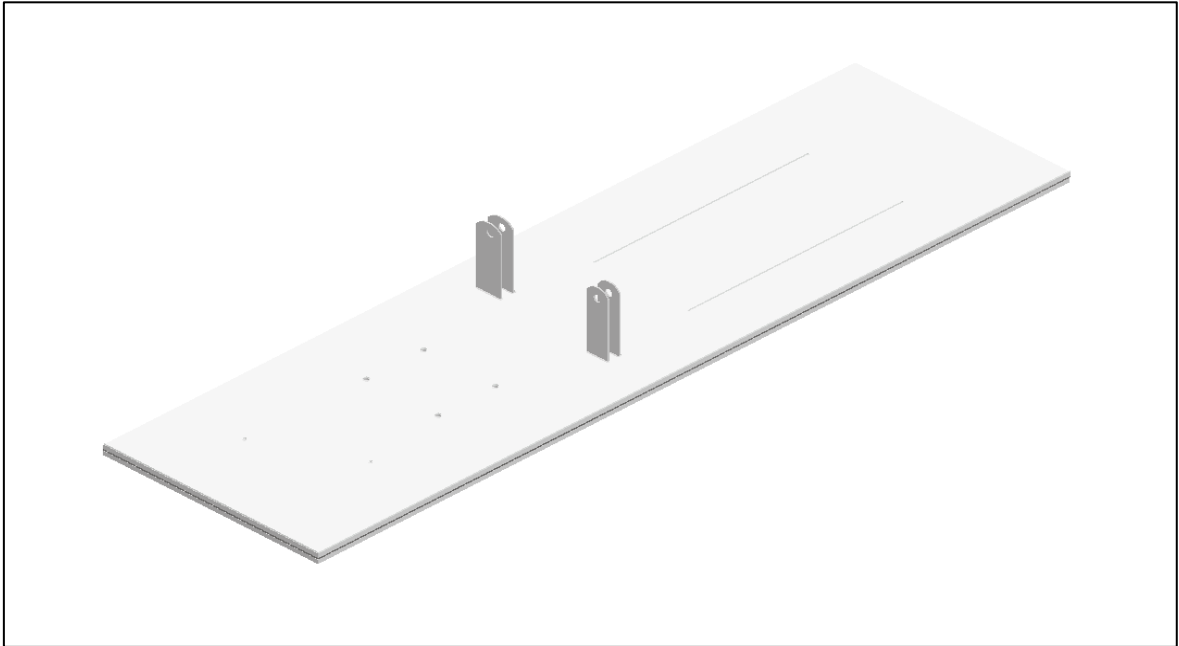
Diseño de la estructura del tablero del sistema de carga
